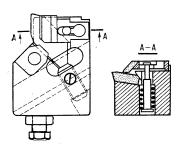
Резец конструкции ВНИИ с твердосплавной пластинкой.
